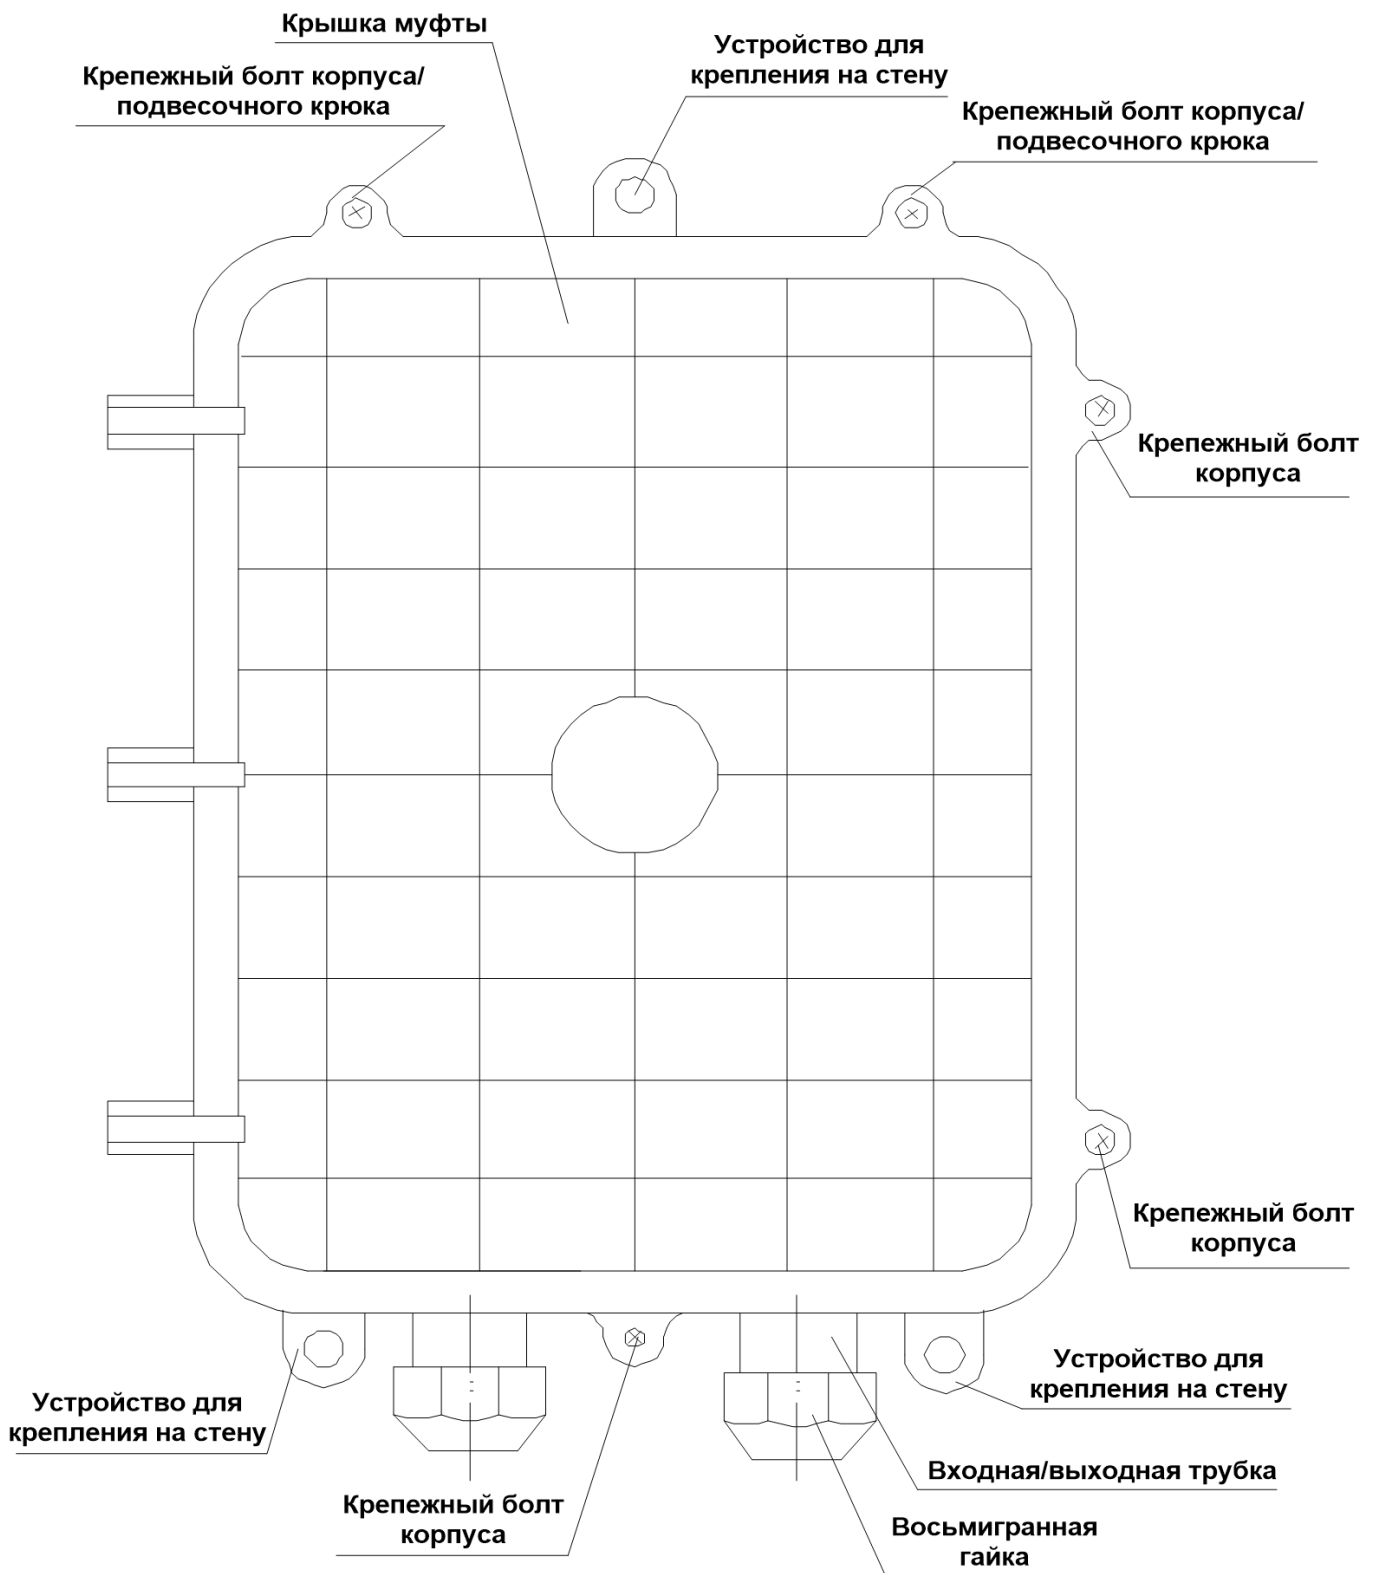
Сборка корпуса муфты и ее закрепление на определенном месте
